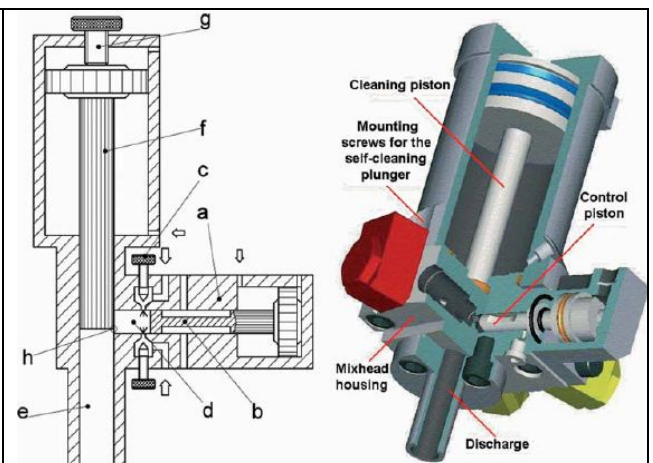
Слева: Схема Г-образной смесительной головки с механизмом регулирования зазора дозирования: (а: камера смешения; b: поршень регулировочно-чистящий с циркуляцией; d: камера смешения; e: разгрузочный канал; f: поршень регулировочно-чистящий; g: механизм для регулировки зазора и расхода жидкости; h: зазор между секциями). Справа: трехмерная модель в разрезе САПР (источник: Cannon)
